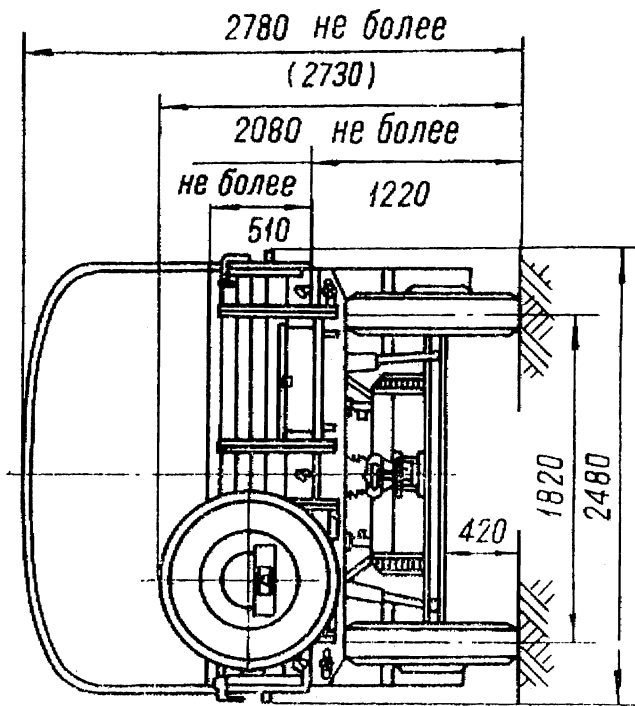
Тягово-сцепное устройство и привод поворота колёс прицепов СМЗ-8325 и СМЗ-8326
